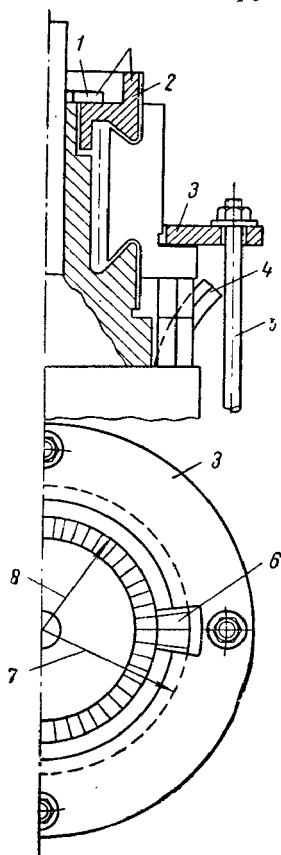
Приспособление для замены неисправных пластин коллектора:
